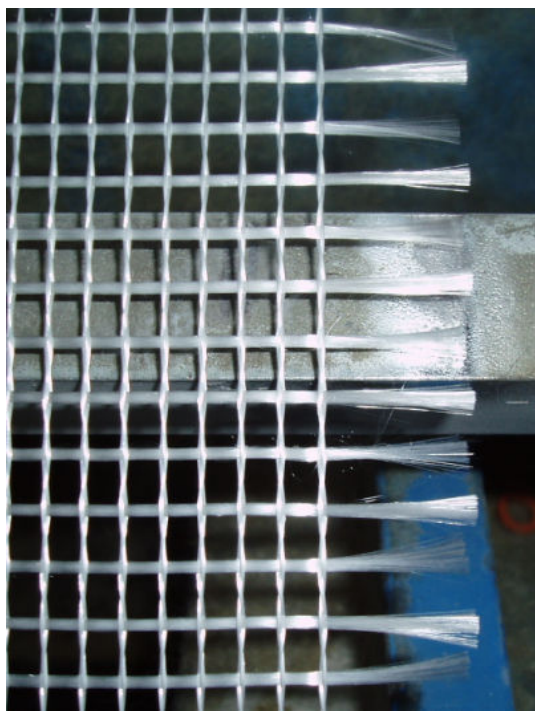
Detail paprsku tkacího stroje – po úpravě
